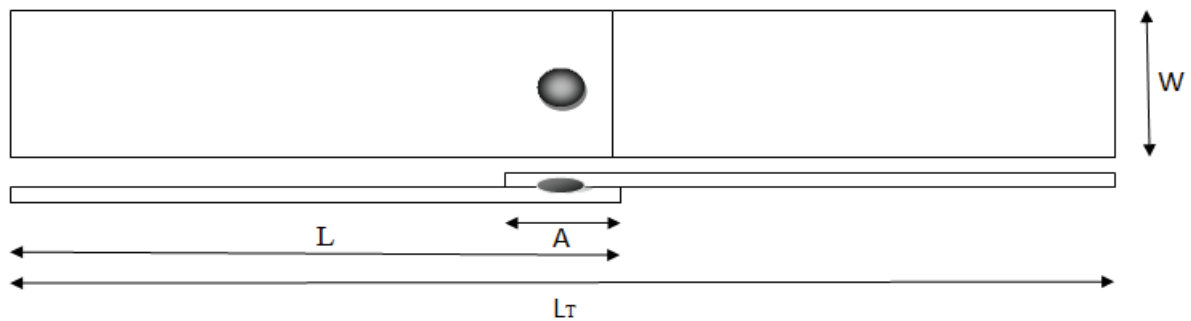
Dimension des éprouvettes soudées.
